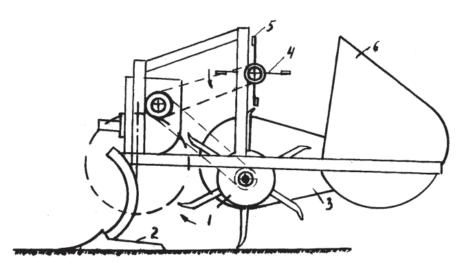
Орудие для извлечения и сбора корневищевых сорняков Г.М. Рудаковаю: 1- ротор; 2- лапа культиватора; 3- кожух привода; 4, 5- битер; 6- бункер
